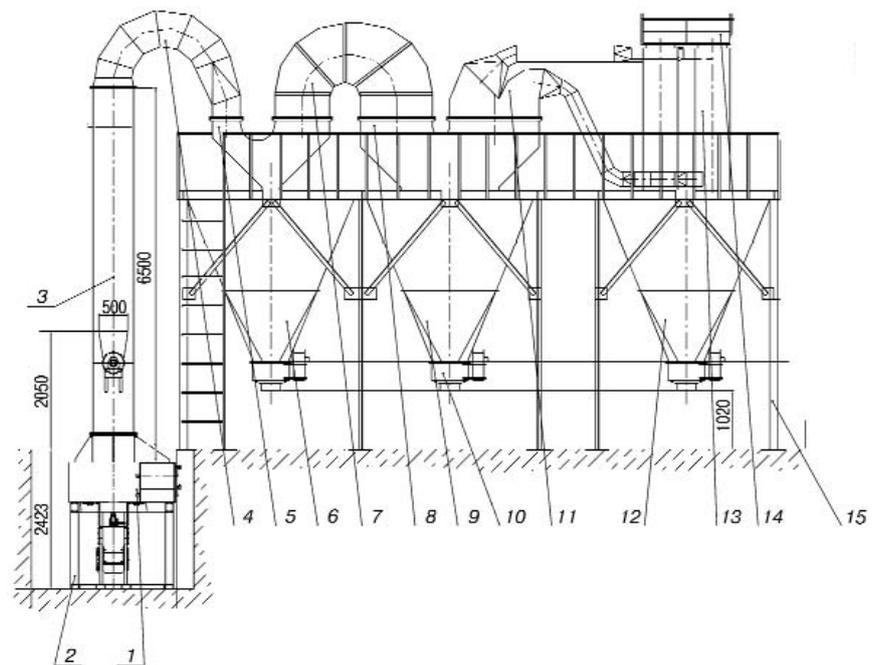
Измельчительно-сушильный агрегат: 1 – активационная камера; 2 – опорная рама; 3 – сушильная камера; 4 – переходник; 5 – пылеулавливатель инерционный I ступени; 6, 9, 12 – бункеры; 7 – короб соединительный; 8 – пылеулавливатель инерционный II ступени; 10 – питатель; 11 – коллектор; 13 – циклон ВЗП; 14 – короб отводящий; 15 – стойка бункеров
